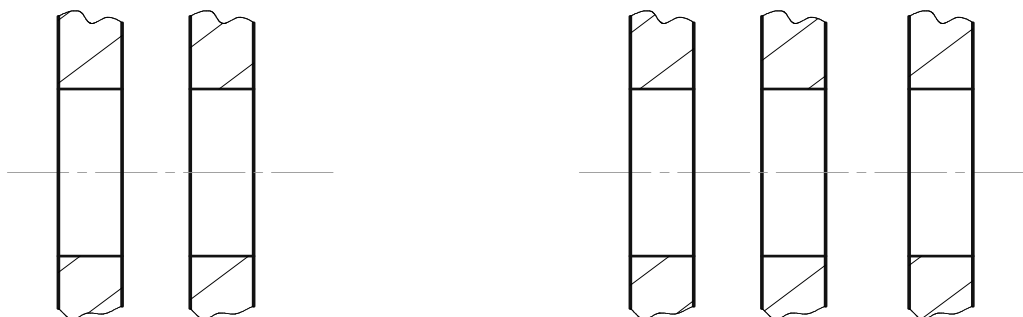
К вопросу о расположении и размерах диаметров отверстий в противоположных и промежуточных стенках корпусной детали
